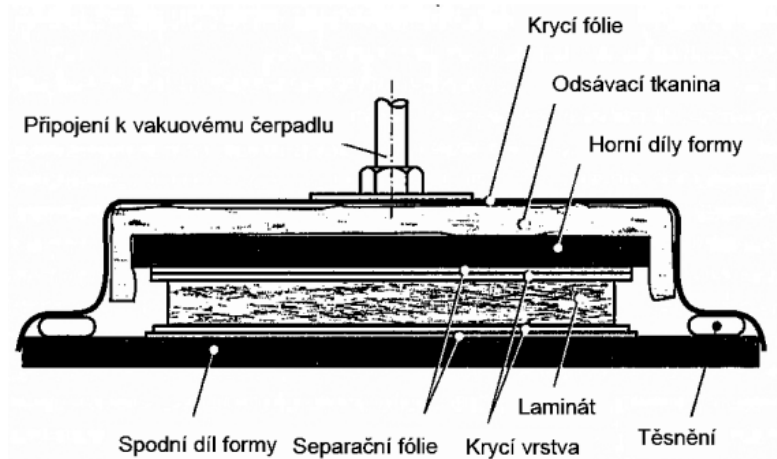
Nízko tlaká (vakuová) technologie výroby prosvycováním používající jednoduchou formu. [26]
